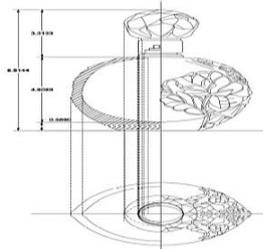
مسقط رأسي وأفقي وقطاع للفكرة التصميمية الثالثة
